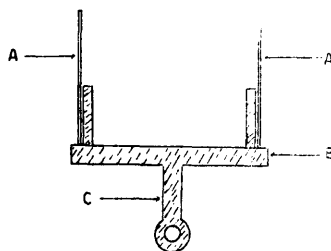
Metade da "moldeira" que se pode observar à Fig. 3.
